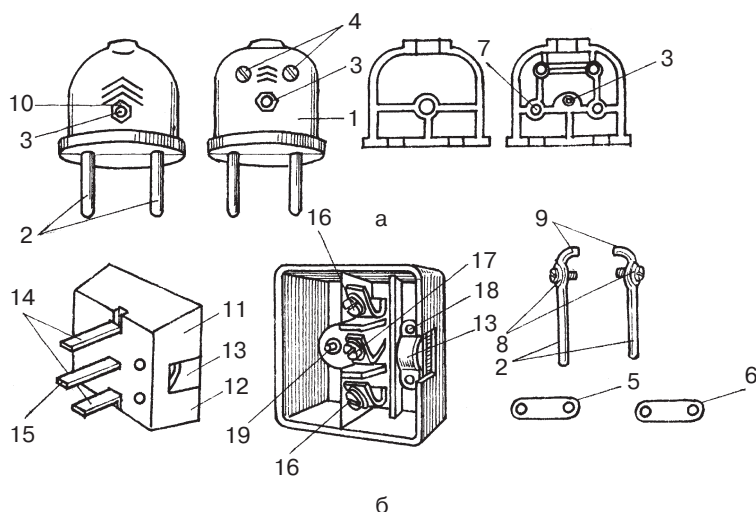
Устройство штепсельной вилки: а — вилка с круглыми рожами (1 — корпус; 2 — круглые рожки; 3 — винт; 4 — винты; 5 — скобка для закрепления шнура; 6 — изоляция под скобку; 7 — углубление в корпусе; 8 — винт с шайбой для присоединения жилы шнура; 9 — выступ; 10 — гайка); б — вилка с тремя плоскими рожами (11 — корпус; 12 — крышка; 13 — скобка; 14 — короткие рожки; 15 — защитный рожек; 16, 17, 18, 19 — винты)
